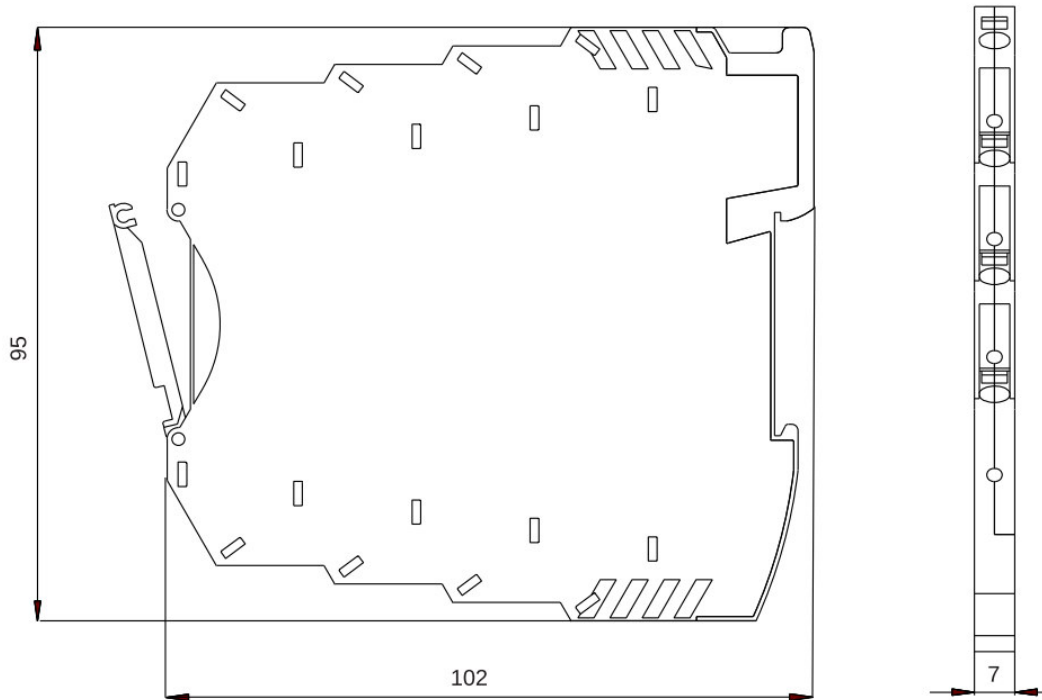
Габаритный чертеж ЕТР-431
